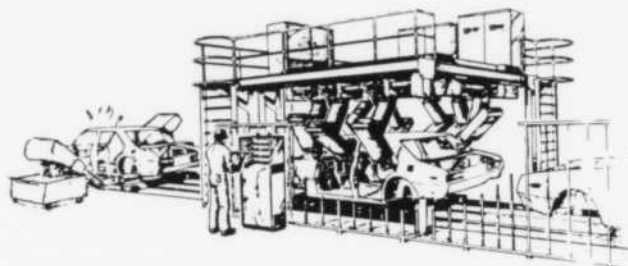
Cellule de soudage robotisée dans l'industrie automobile.
